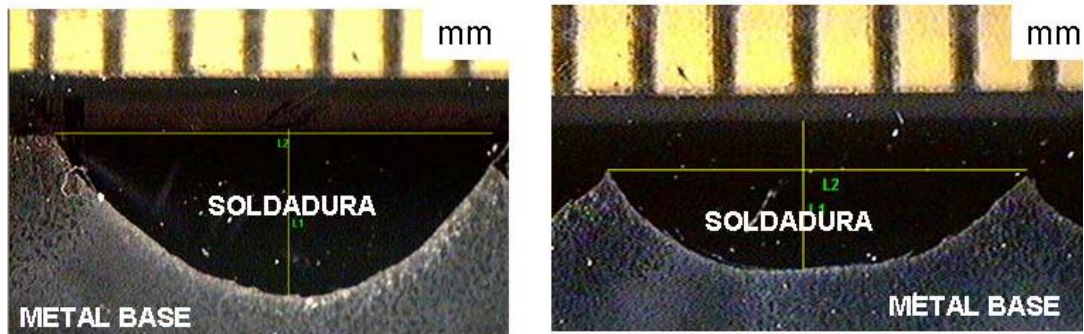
Muestras de soldadura a) Macroataque donde se muestra la penetración, nital 10%
